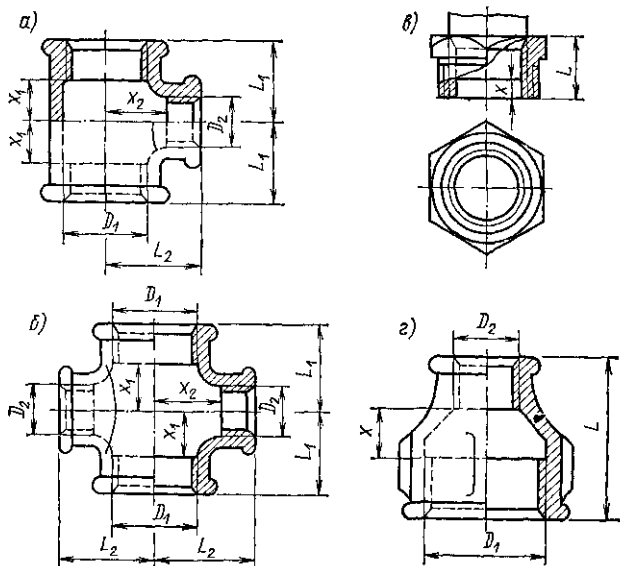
Соединительные части из ковкого чугуна (переходные)
